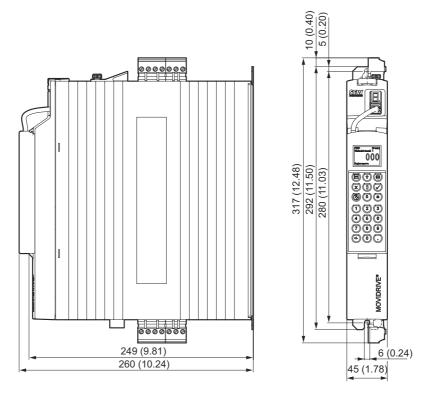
Dimensões MDX60B, tamanho 0S, dimensões em mm (in)
